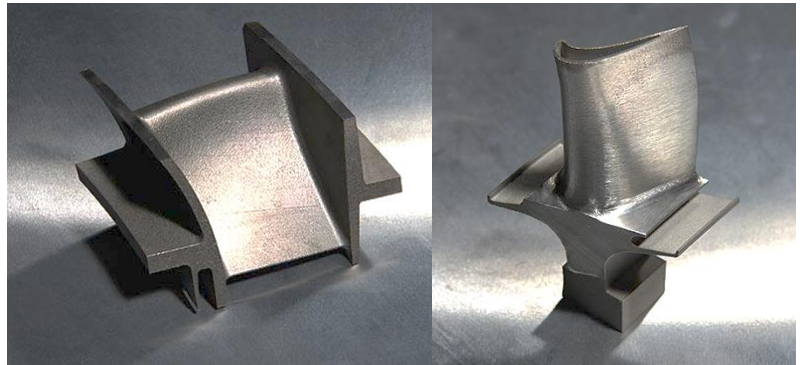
Лопатка холодной части для перспективного турбореактивного двигателя семейства ПД (слева) и лопатки турбины высокого давления для перспективного двигателя семейства ПД из жаропрочного сплава, полученные селективным лазерным сплавлением из жаропрочного сплава
